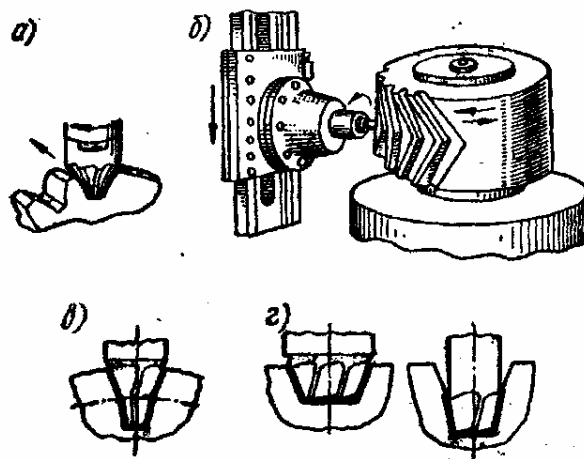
Нарезание зубьев зубчатых колес пальцевыми фрезами: *a* – прямозубого колеса; *b* – шевронного колеса; *в* – черновое нарезание двуугловой фрезой; *г* – последовательно двумя угловыми фрезами
